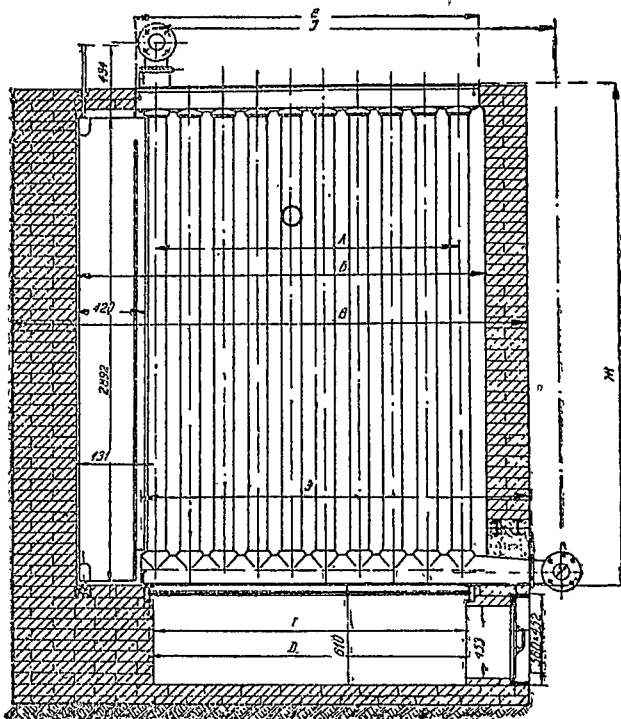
Общий вид гладкотрубного вертикального водоподогревателя системы Грина.
